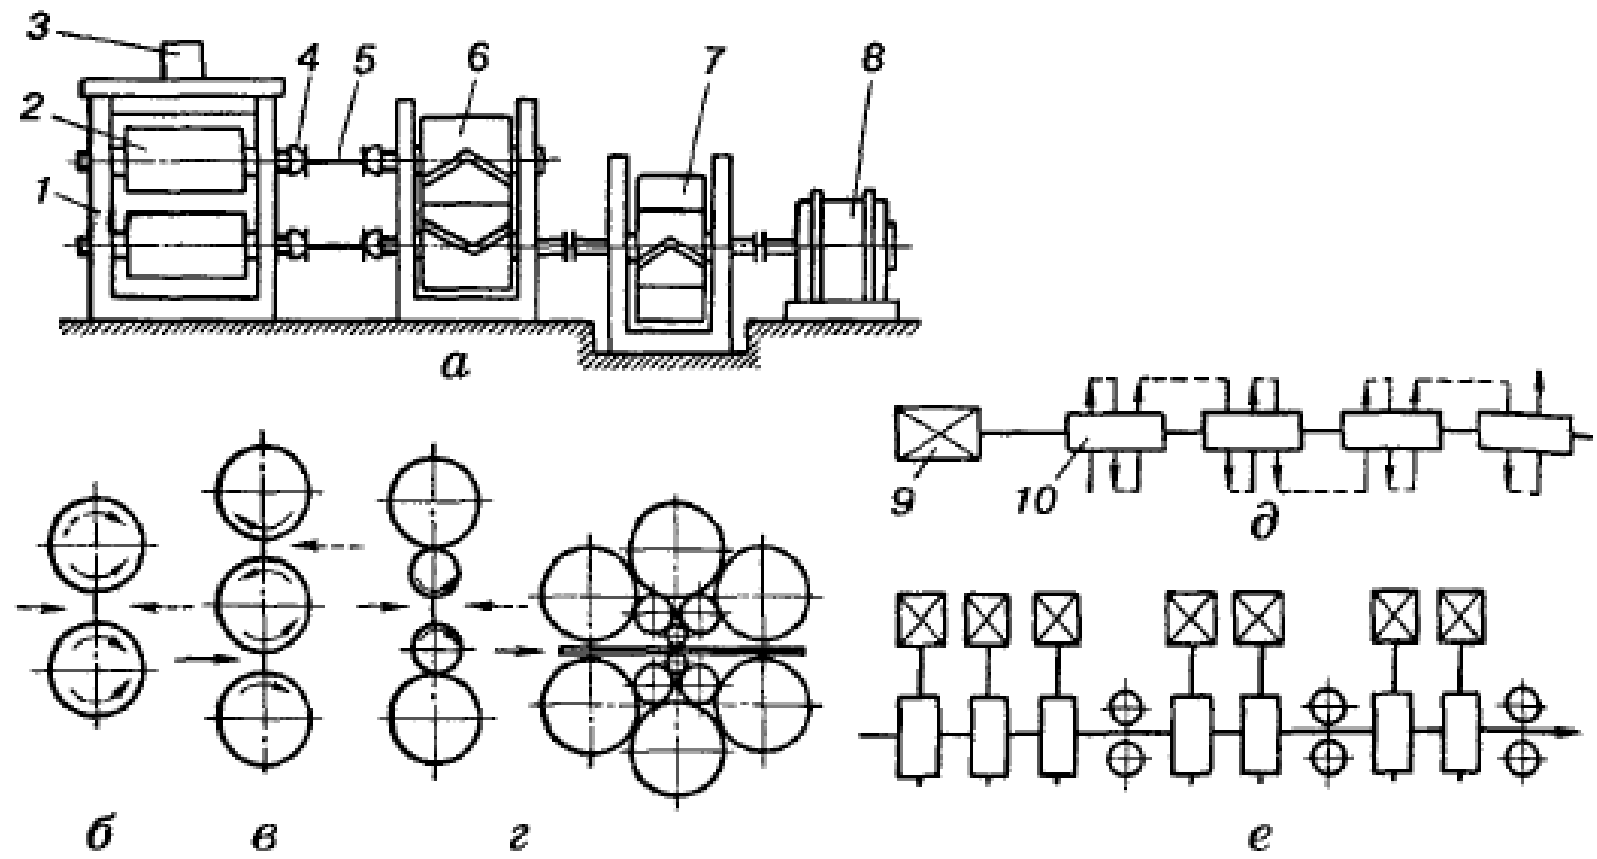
Схеми прокатного стану, розташування валків і робочих клітей
